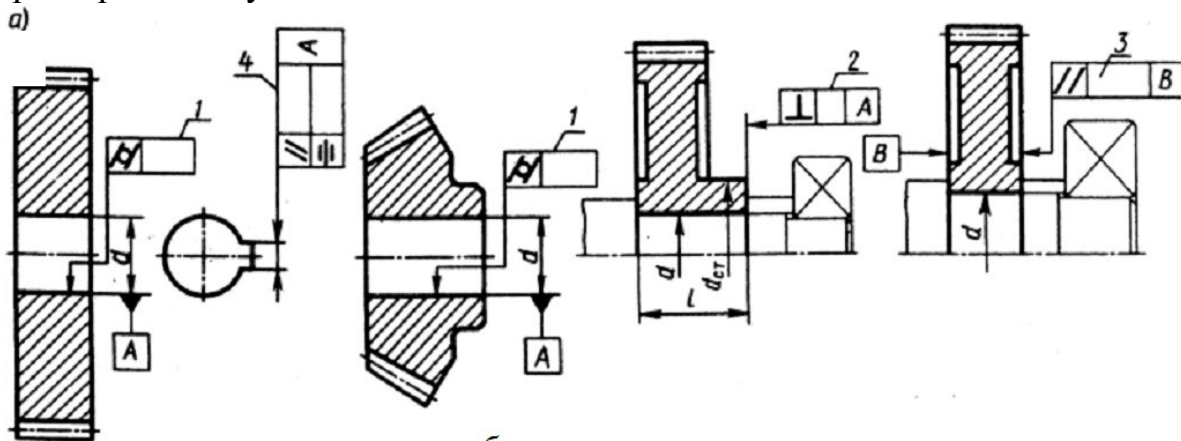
Параметры формы и расположения поверхностей зубчатых колес, указываемые на чертежах
